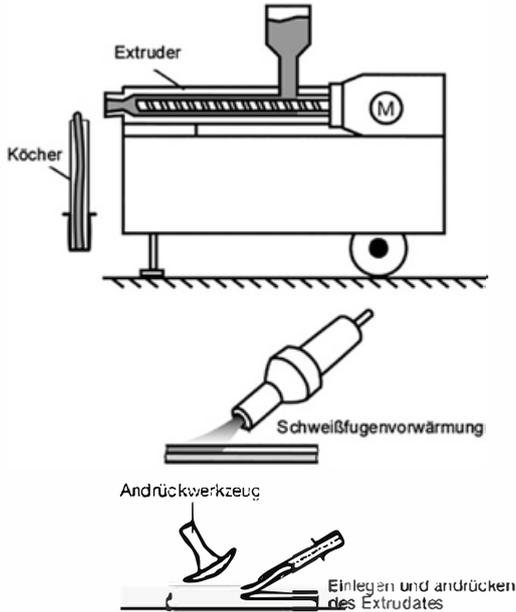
Schema diskontinuierliches Schweißen mit Maschinenvariante II.
